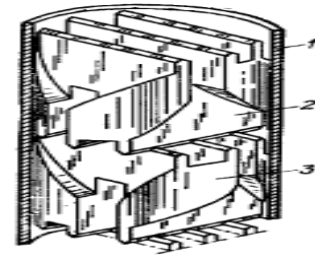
Смеситель с решетчатым расположением пластинчатых элементов: 1 – корпус; 2, 3 – пластинчатые элементы
